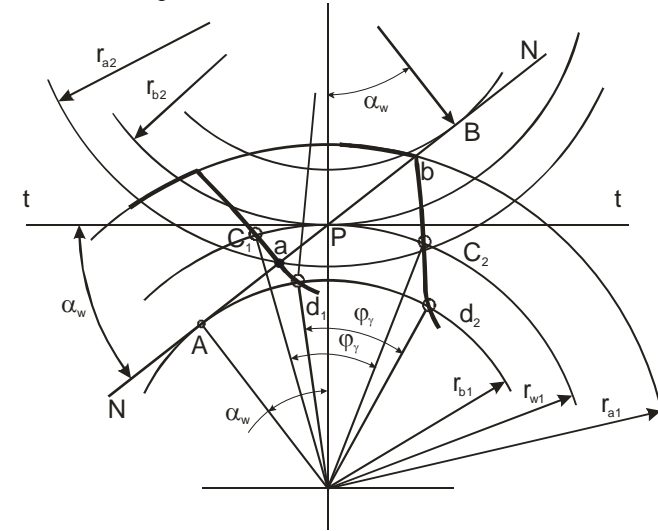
Зацепление зуба шестерни с зубом колеса
